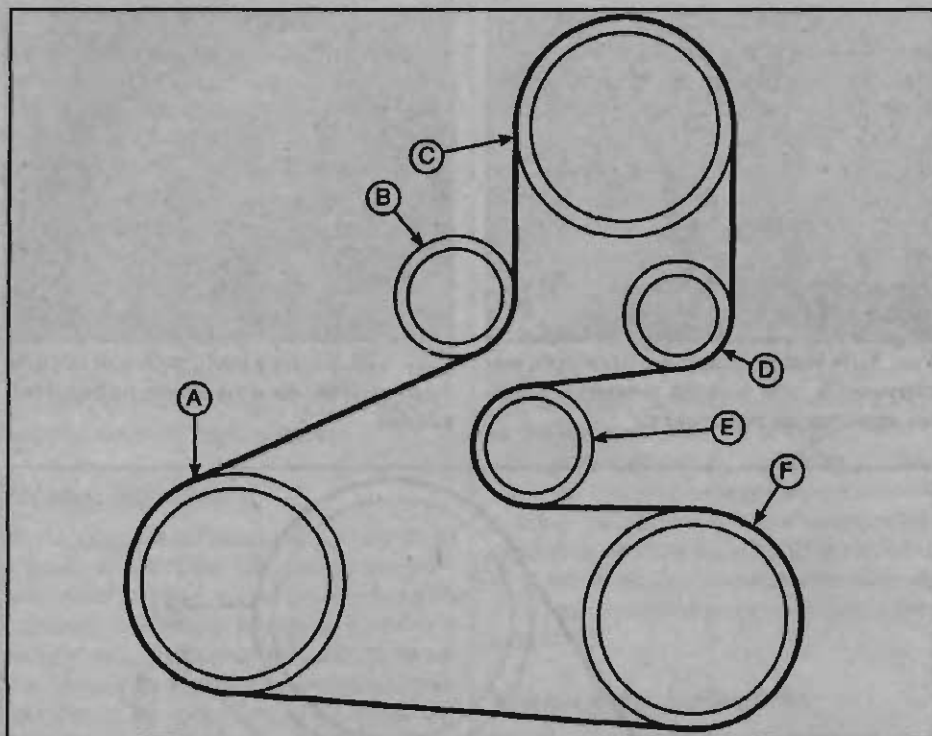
Расположение ремня привода навесных агрегатов на шкивах двигателя 1,6 л с системой кондиционирования воздуха: А – шкив коленчатого вала; В – шкив автоматического механизма натяжения ремня; С – шкив насоса усилителя рулевого управления; D – шкив генератора; E – направляющий шкив; F – шкив компрессора системы кондиционирования воздуха
